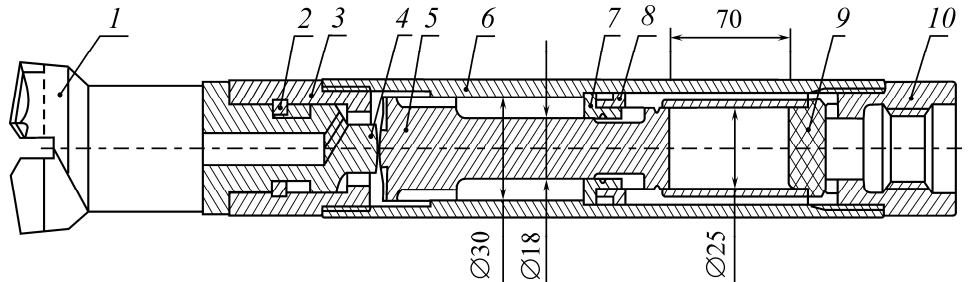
Пневмоударник АШ-46А: 1 — буровая коронка; 2 — кольцо; 3 — гайка передняя; 4 — бусса; 5 — ударник; 6 — корпус; 7 — втулка разрезная; 8 — гильза; 9 — пробка; 10 — гайка задняя
